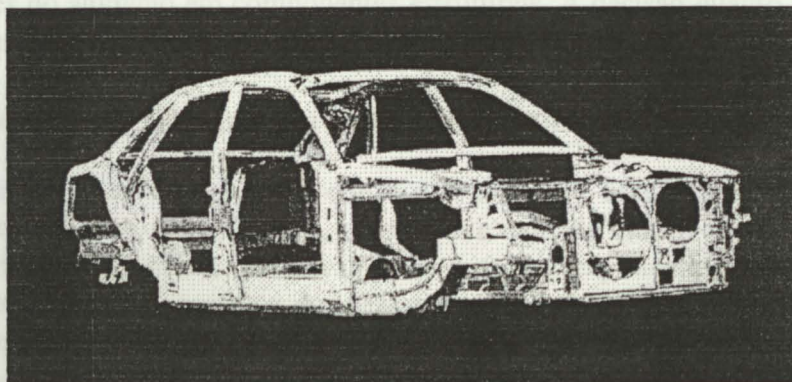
Estrutura tubular tipo *space frame* (*AUDI ASF Concept Car*)
